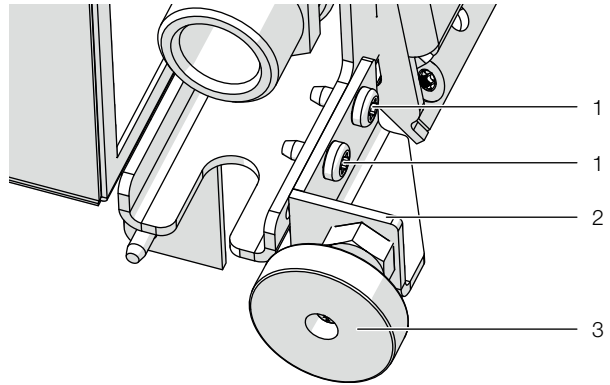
Befestigung des Montagefußes (hier obere Position)
